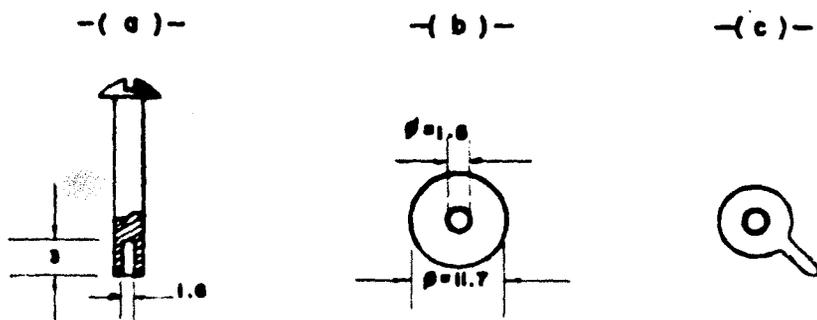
Dimensiones del poste de montaje y disco de acoplamiento al diodo (en mm). También se muestra la zapa de polarización.
